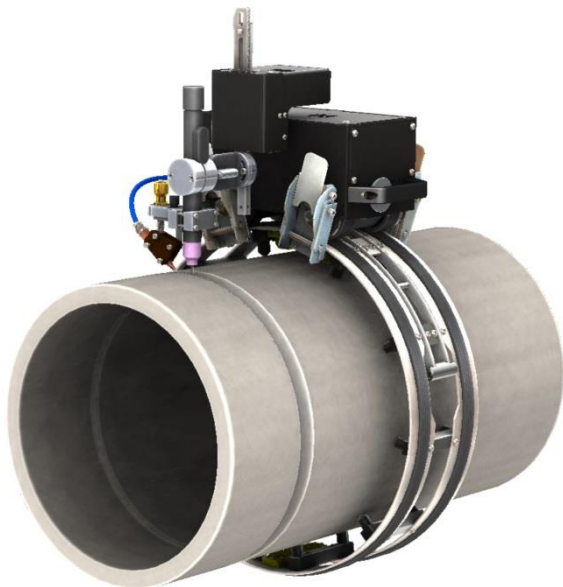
Manipulador robótico utilizado em procedimentos de soldagem orbital.
